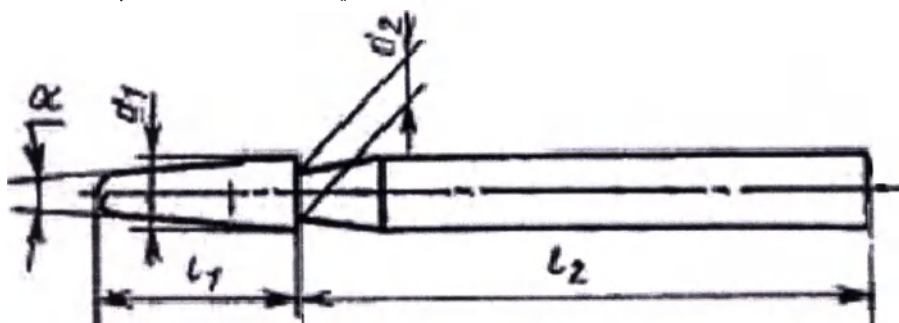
Тип нарезки режущей кромки рабочей фрезы с мелкой нарезкой.
